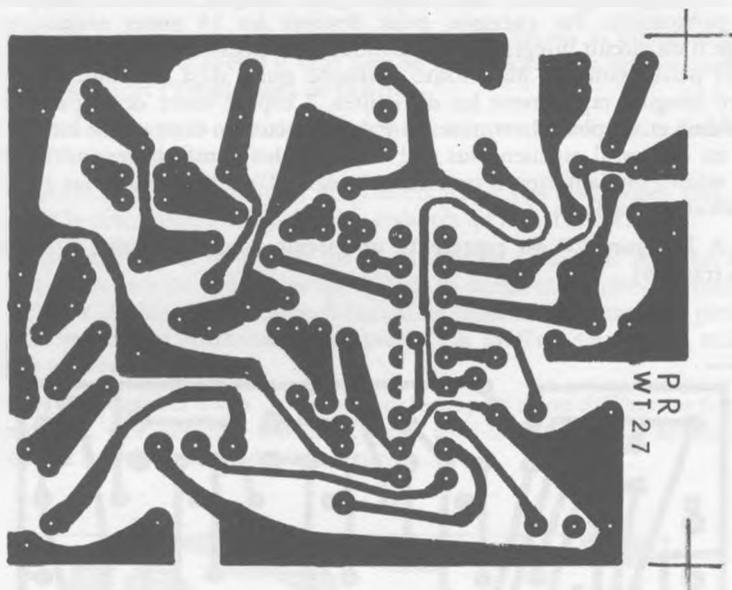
Circuit imprimé dessiné avec un stylo marqueur et des pastilles.
